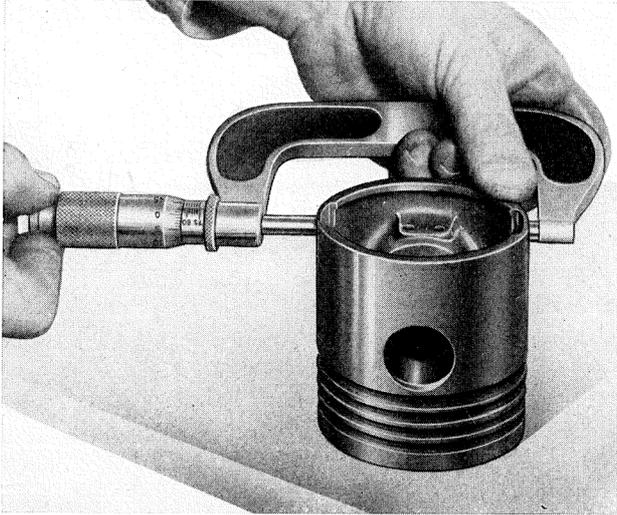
Mesure du diamètre du piston pour déterminer l'usure de la jupe.
